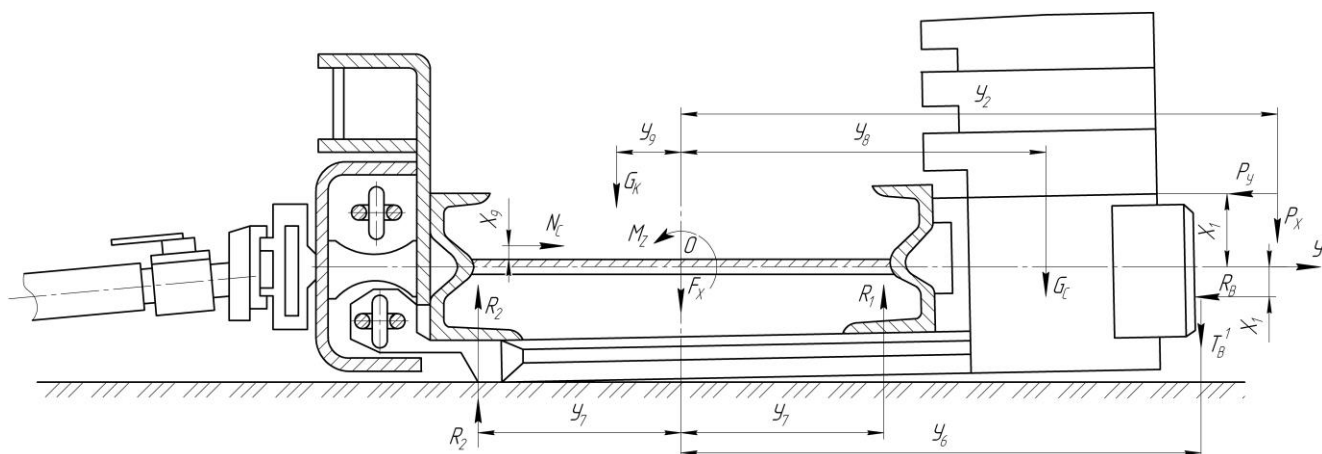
Схема для расчета сил трения в опорах исполнительного органа струговой установки отрывного типа
